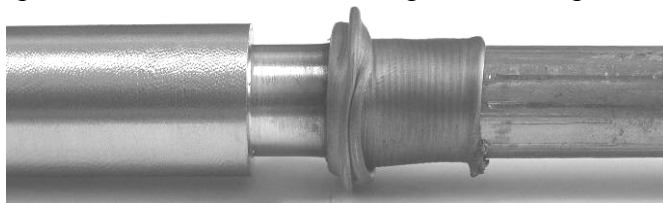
Вигляд зварного з'єднання сталь 12Х18Н10Т-титан ВТ1-0
